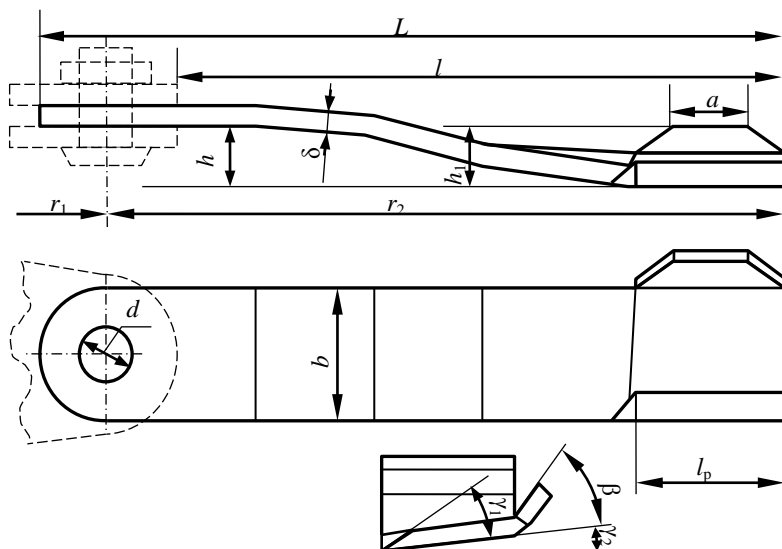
Схема с основными параметрами ножа косилки-измельчителя
